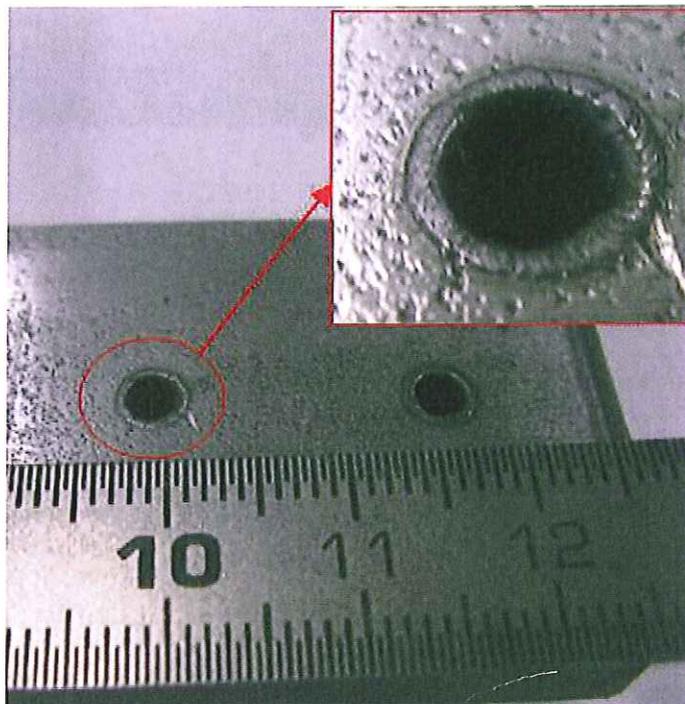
Soudage laser de fins tubes en inox sur un support massif
